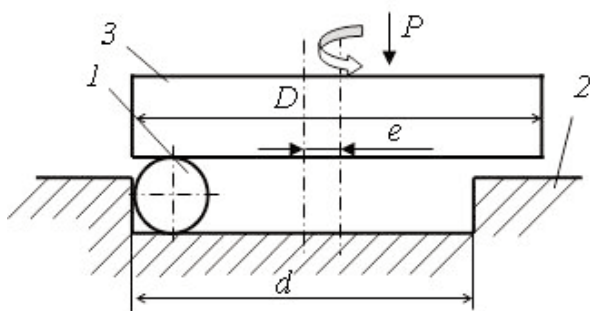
Схема накатывания сферической заготовки плоскими поверхностями
